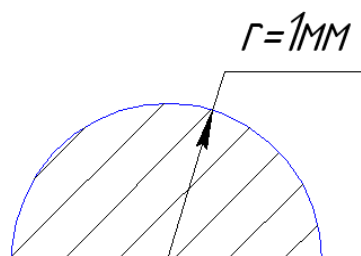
Прийняті форма та розмір наплавленого шва металу навкруг зношених поверхонь отворів
